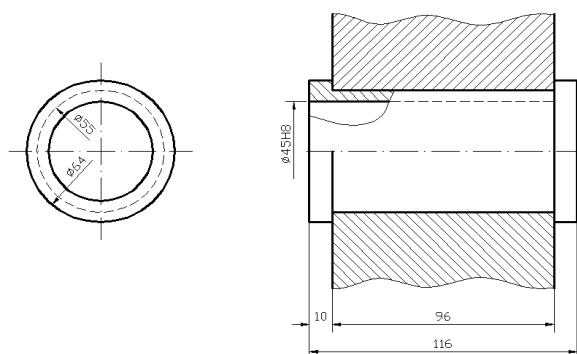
Рабочий эскиз бронзовой ведущей втулки, подлежащей механической обработке при помощи ППД
